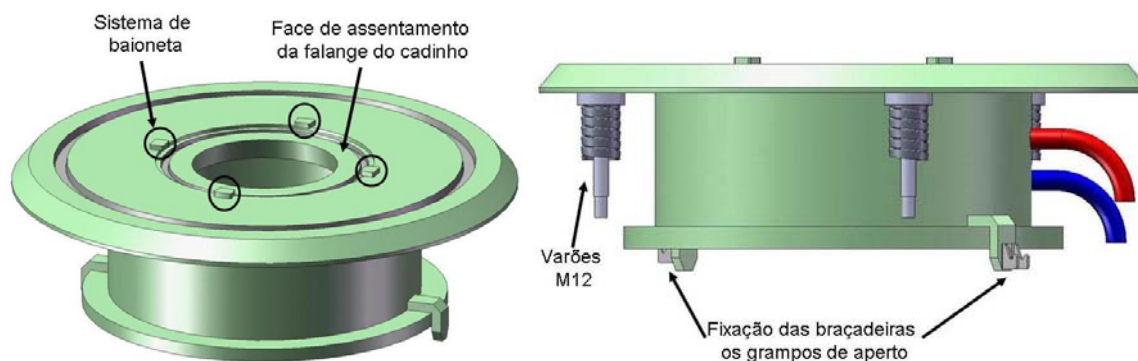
Aspecto do sistema de fixação da câmara de vazamento superior na estrutura de elevação, e do sistema de baioneta.
